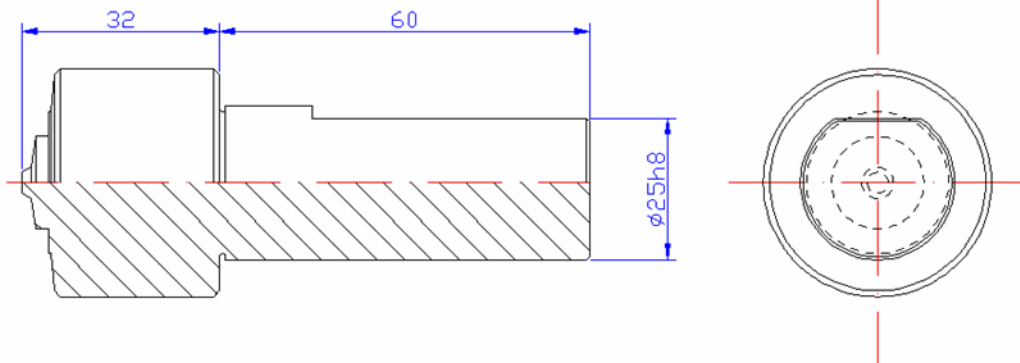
Döner parça tıpası (The rotating part plug)
